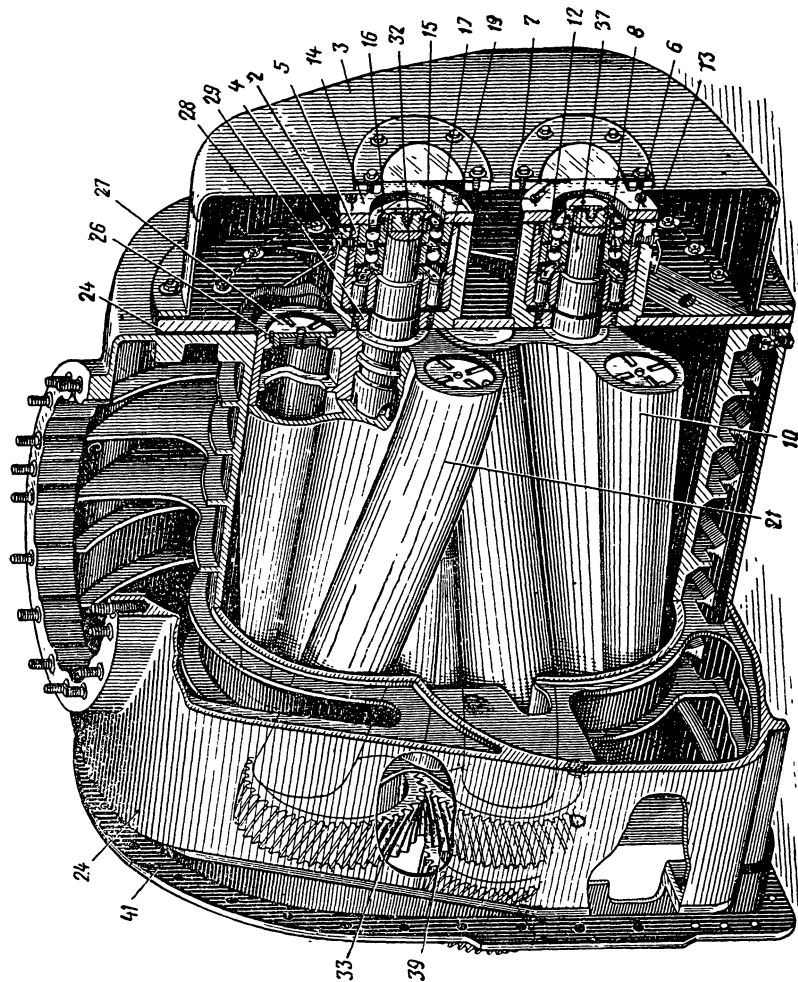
Продольный разрез воздухоудки (обозначения см. на рис. 57)
